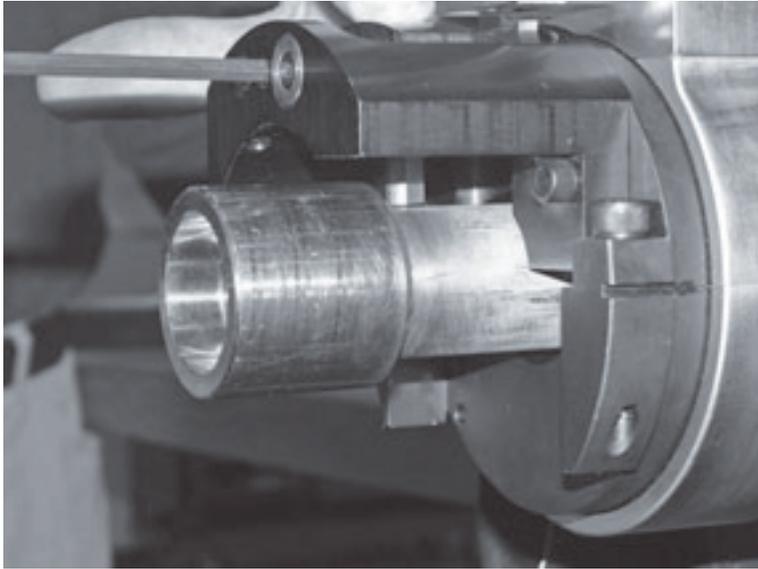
La foto muestra el portaherramientas axial para soldadura por encastre en posición para eliminar la soldadura por encastre.
